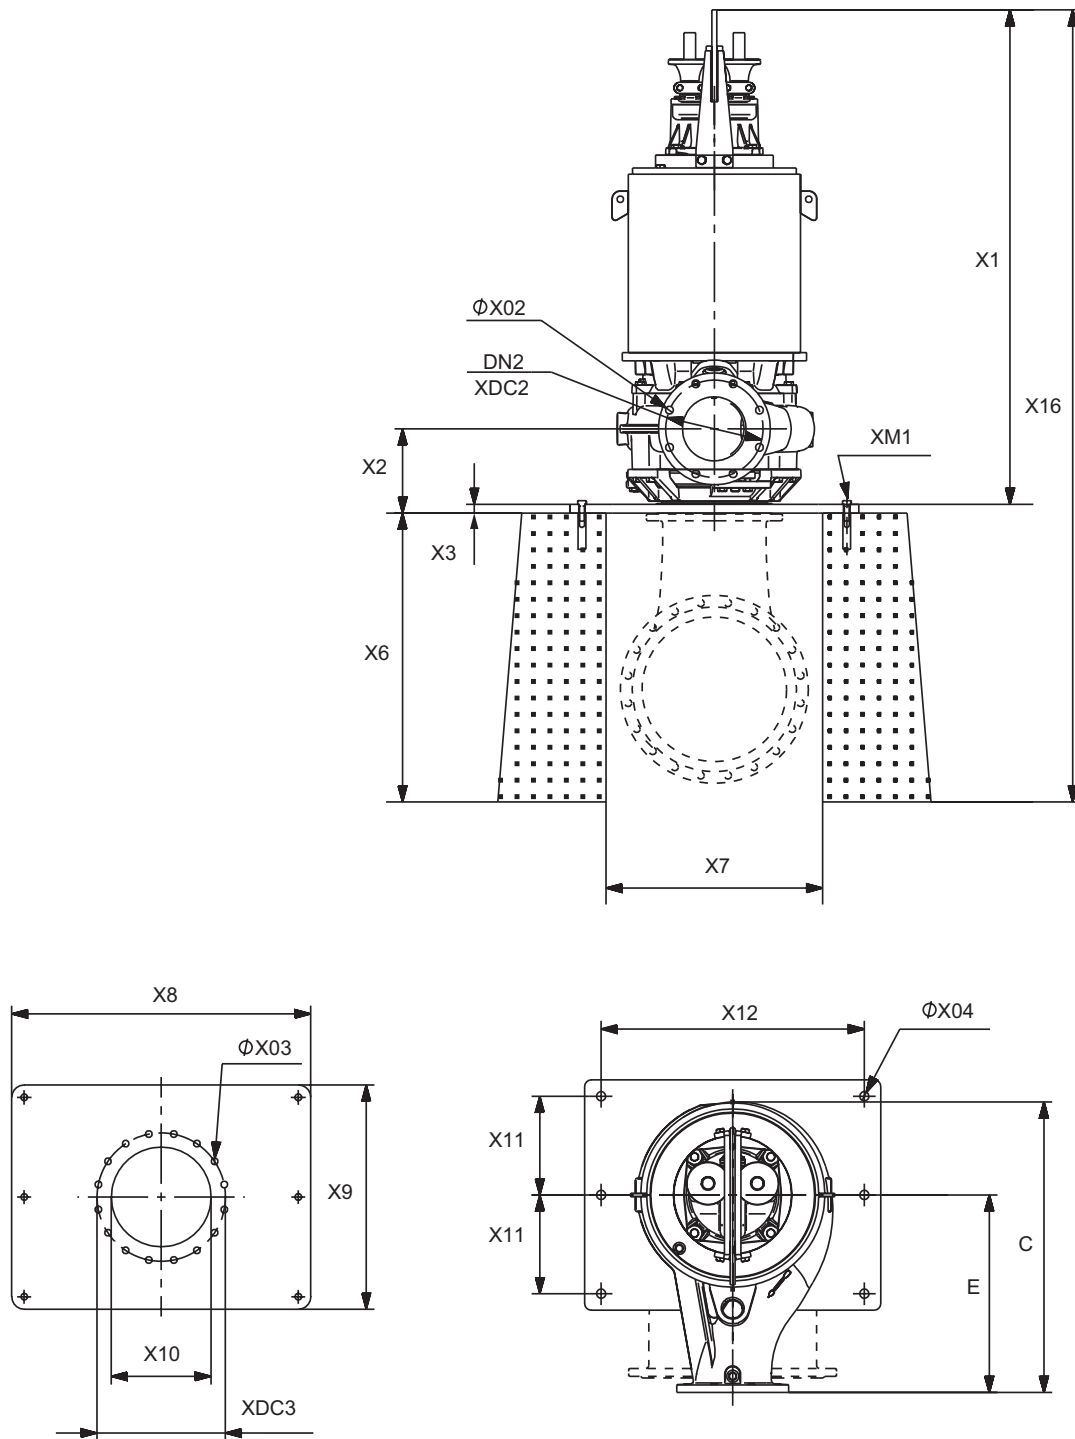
«Сухая» вертикальная установка на фундаменте.
